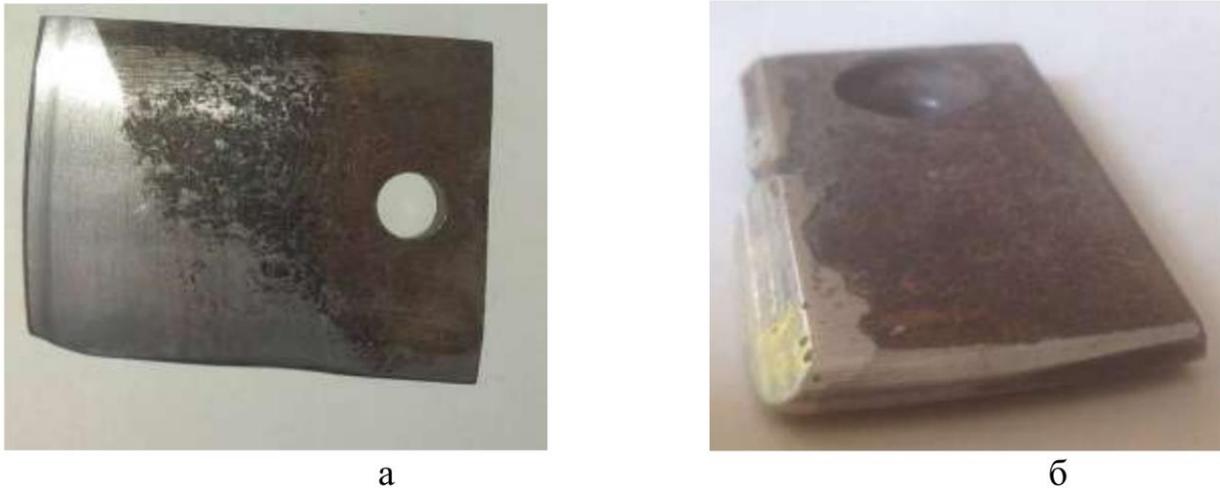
Стан поверхонь зразків зі сталі 40Х після кріообробки: а — без зміцнення; б — зі зміцненням ріжучої крайки наплавленням.
